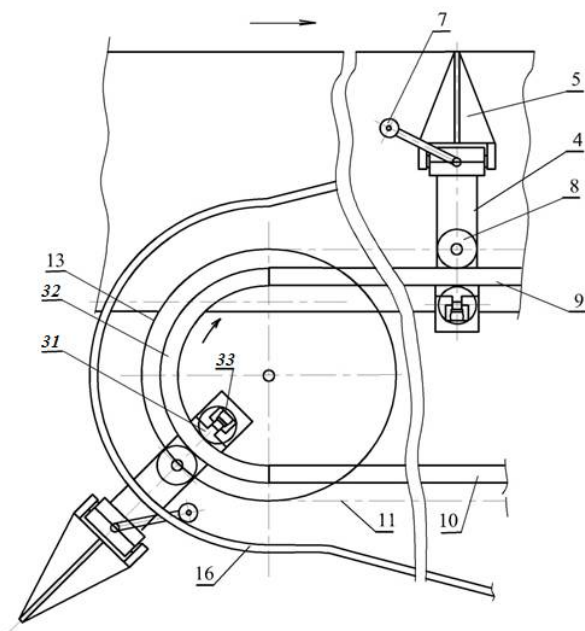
Схема установки дополнительных катков на ходовой опоре
